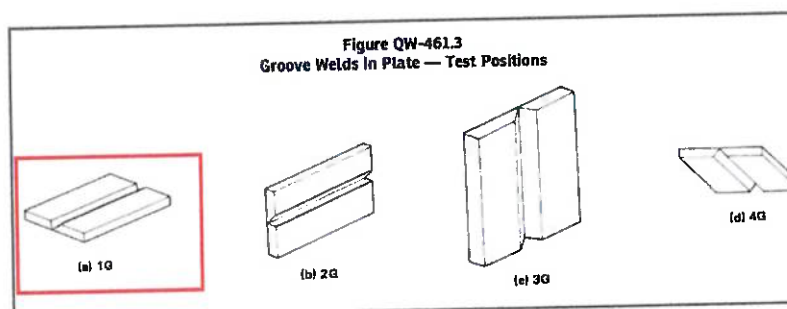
Posição de soldagem 1G- Plana (ASME Section IX -American Society of Mechanical Engineers Welding and Brazing Qualifications,, 2013)
